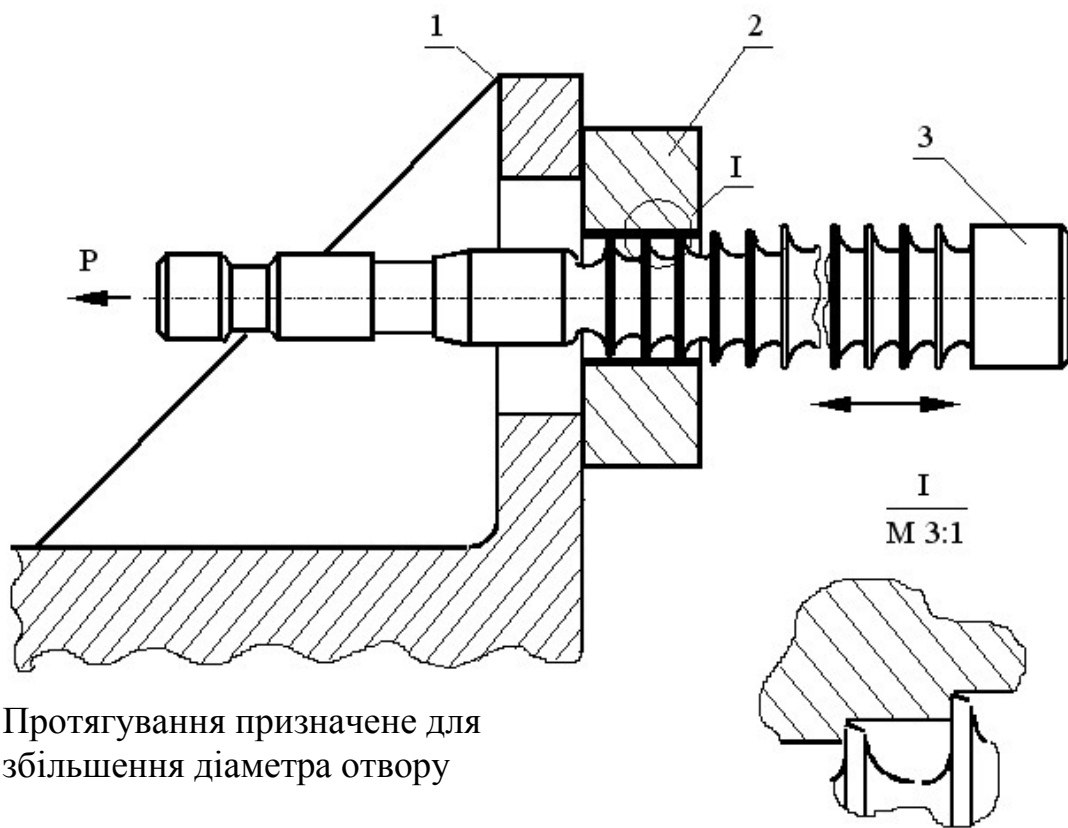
Схема протягування отвору: 1 – кронштейн станка; 2 – заготовка; 3 – протяжка
